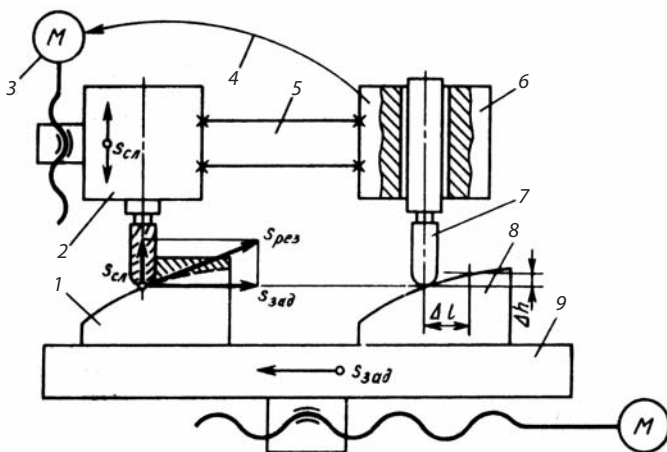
Принцип работы следящей копировальной системы фрезерного станка
